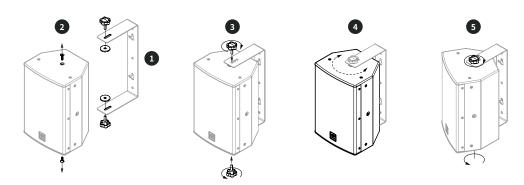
COX 8 MKII - COX 8 MKII - Installazione con staffa di montaggio a parete.
